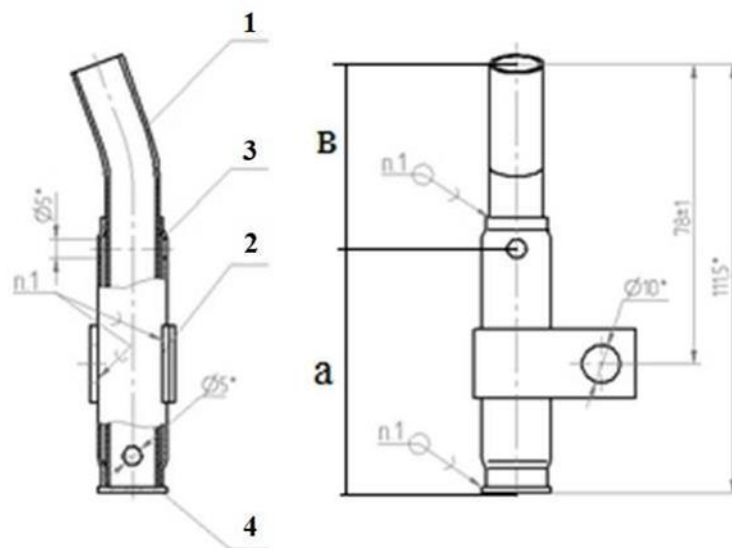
Серійний гідрозатвор СВК V-подібних двигунів 8ЧН 12/13: 1 – трубка; 2 – клямер; 3 – трубка; 4 – заглушка
